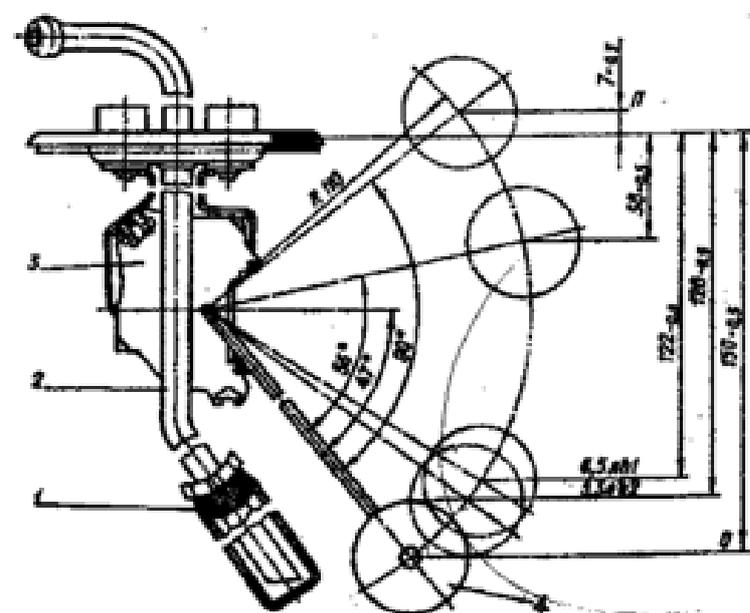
Датчик указателя уровня топлива: 1 - фильтр; 2 - трубка приемная; 3 - корпус реостата; 4 - поплавок; 0 - бак пустой; 1/2 - половина емкости бака; П - бак полный; h1, h2 - положение поплавка, при котором загорается контрольная лампа резерва топлива на комбинации приборов (если комбинация приборов оборудована такой лампой)
